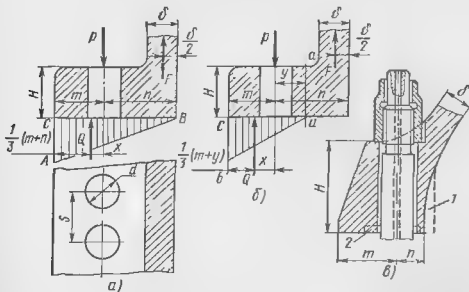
Эскиз к расчету фланца горизонтального разреза цилиндра: а — без изгиба; б — с изгибом; в — фланец ЦВД турбины высоких параметров пара; 1 — внутренний прилив; 2 — разгрузочная наплавка
